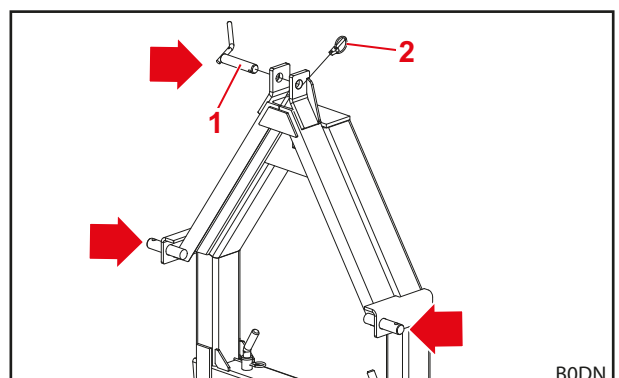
Points de fixation pour le montage à l'arrière du tracteur
